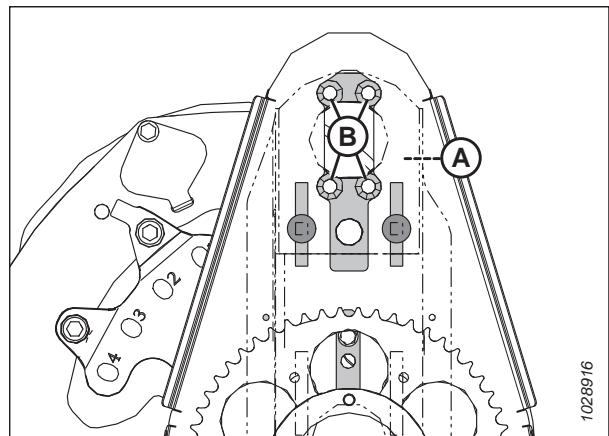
Befestigungsbohrungen des Haspelantriebsmotors
